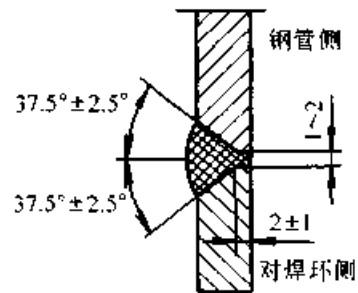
对焊环与钢管连接的焊接接头和坡口尺寸
